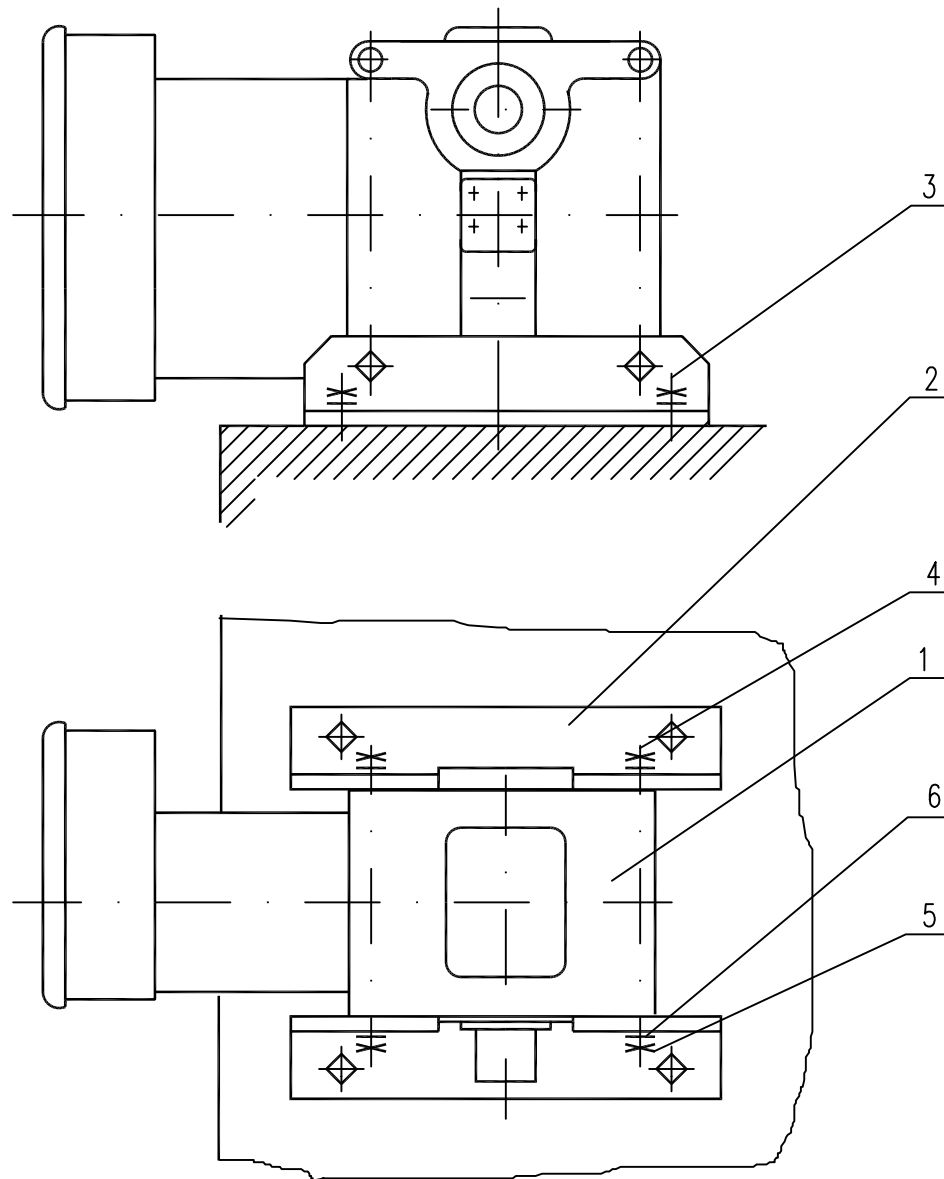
Крепление блока исполнительного приводов типоразмеров ПД-06-08-5УХЛ1 к вертикальной плоскости с горизонтальным расположением выходного вала
